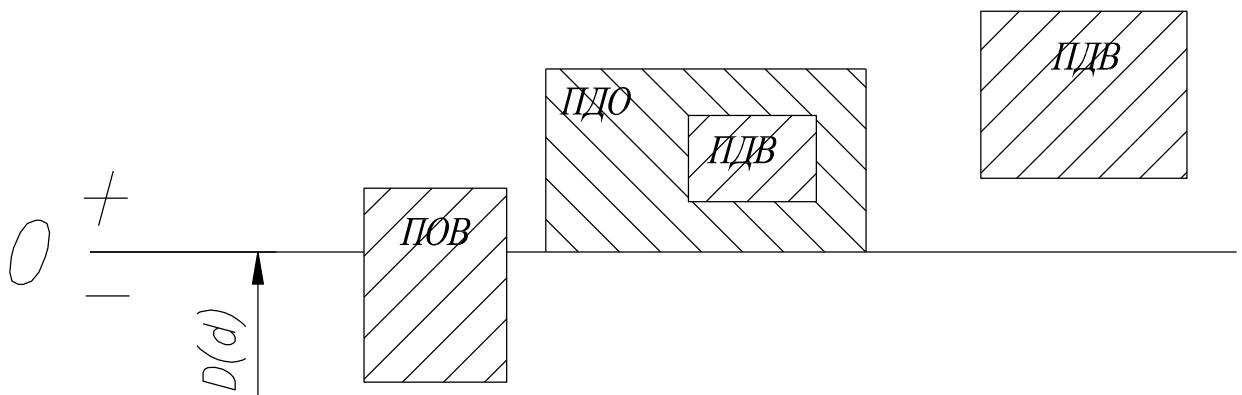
6. Схема розташування полів допусків перехідного з'єднання
